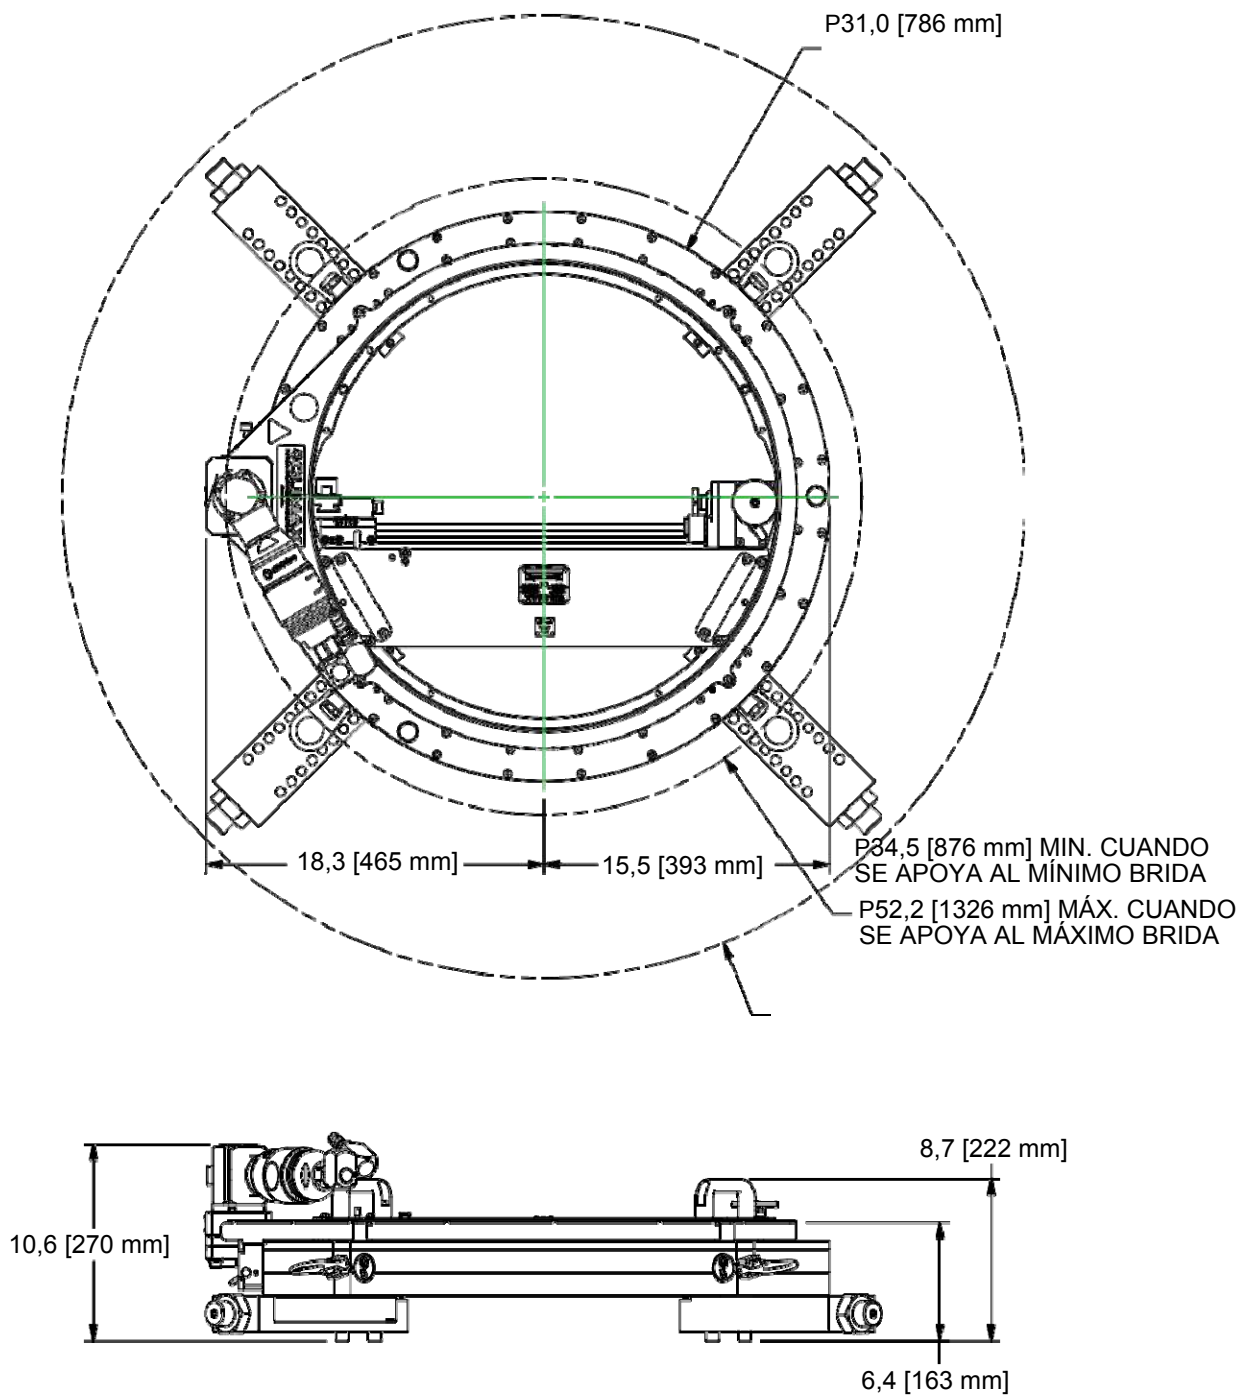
FF3600 DIMENSIONES- DE LA MÁQUINA DE MOTOR NEUMÁTICO DE ÁNGULO RECTO
